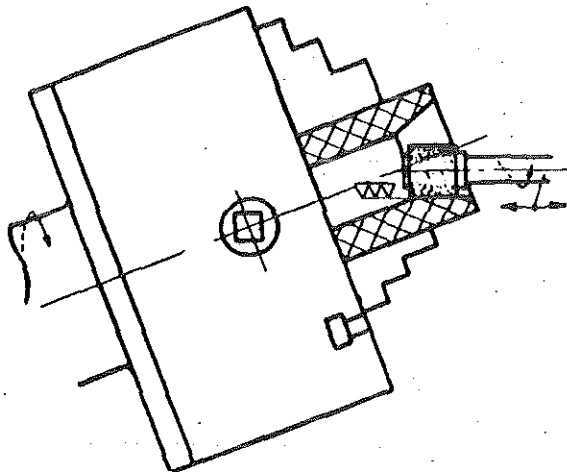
Montagem para peça de qualquer cônica com inclinação do cabeçote.
